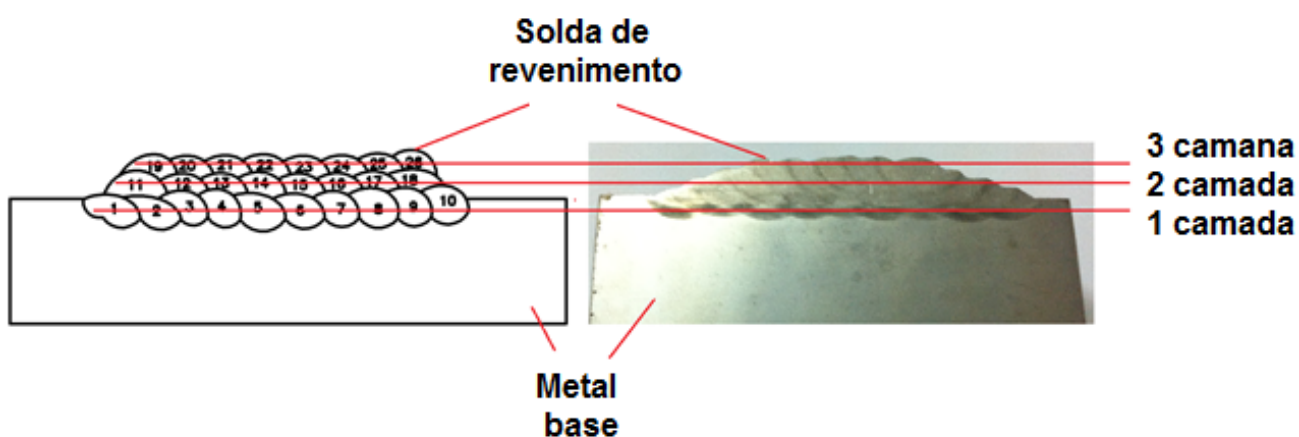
Soldagem com passe de revenimento – corpo de prova.
